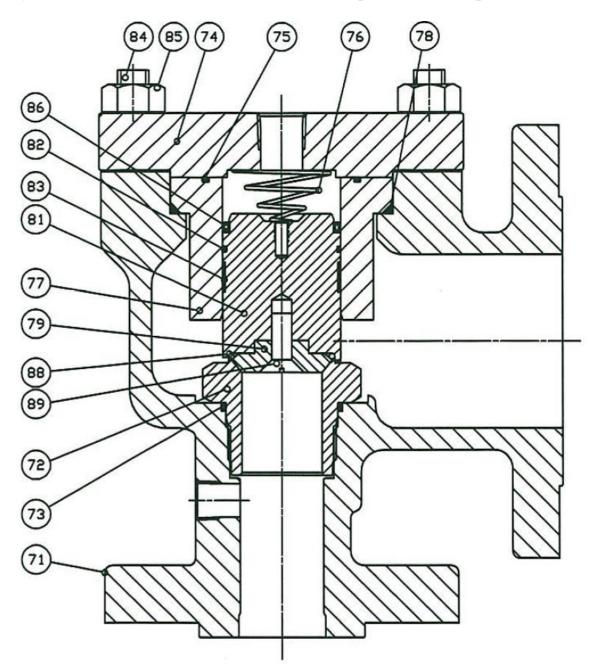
Главный клапан 3900 MPV с мягким уплотнением седла в сборе
